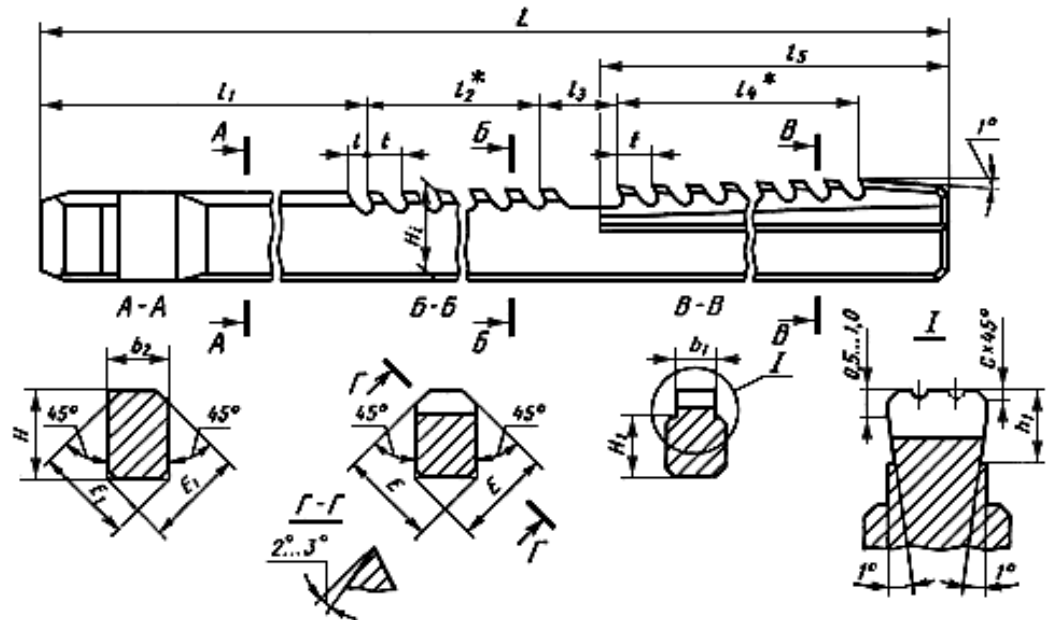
Основні конструктивні розміри робочого інструменту для протягування шпонкового пазу (шпонкової протяжки)
